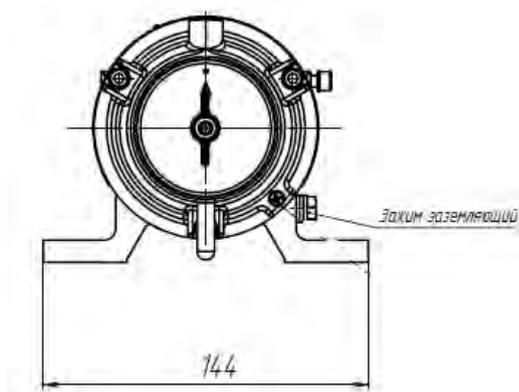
Габаритные размеры ИГМ-14 (корпус тип 4)
